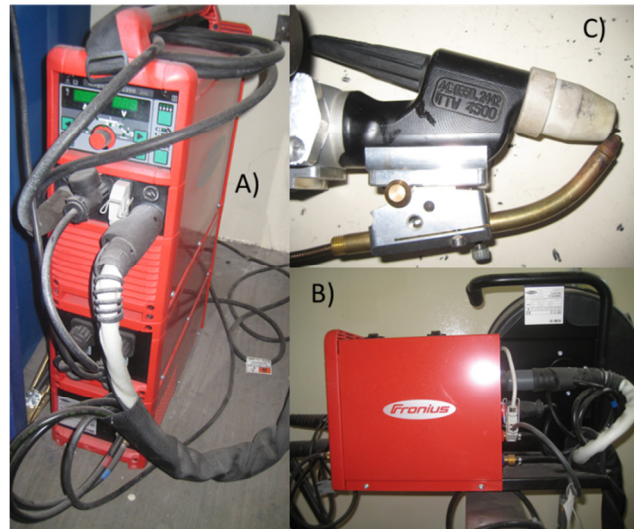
Equipo GTAW cold wire A) Fuente de poder, B) alimentador automático, C) antorcha Robacta.
